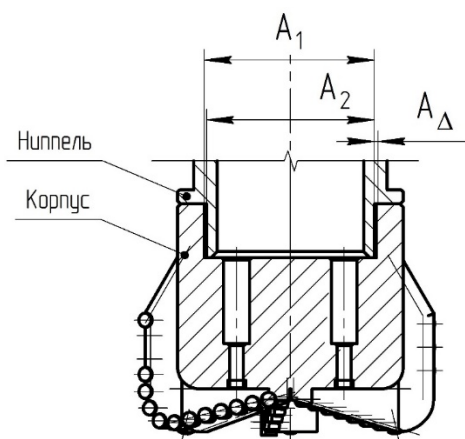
Размерная цепь соединения корпуса с ниппелем
